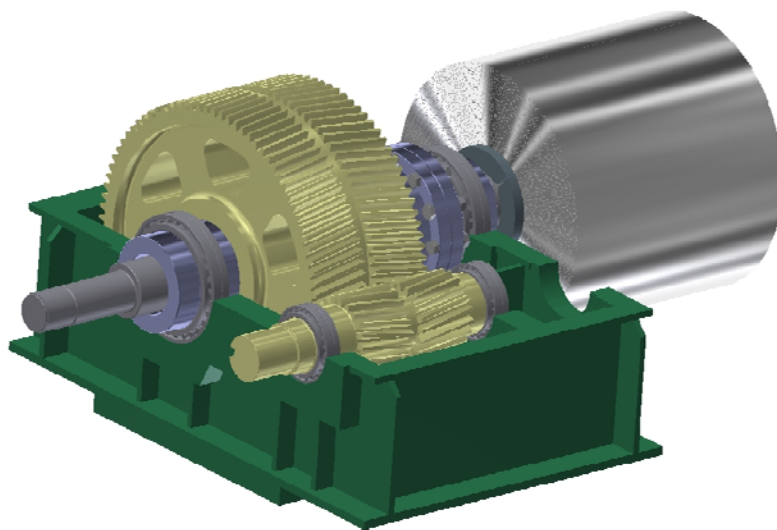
Vista do redutor de uma bobinadeira, em destaque o conjunto de engrenagens bi-helicoidais
